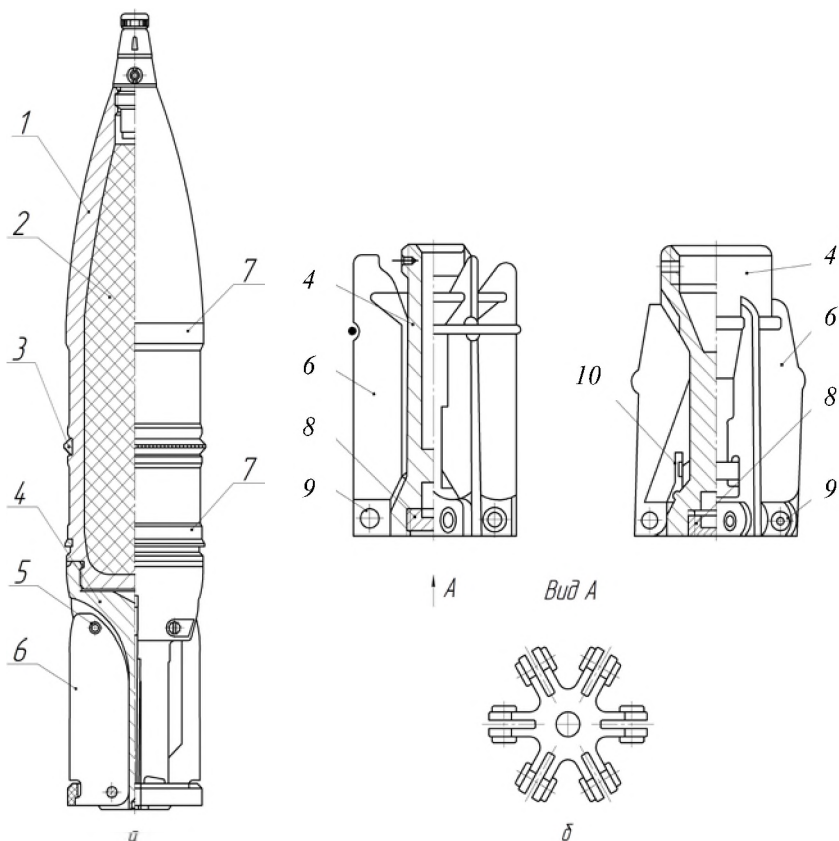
Оперенный снаряд с раскрывающимся стабилизатором второго типа (а) и разновидности раскрывающихся стабилизаторов первого типа (б); 1 – корпус снаряда; 2 – разрывной заряд; 3 – обтюрирующий пояс; 4 – корпус стабилизатора; 5 – стопорный винт; 6 – лопасть стабилизатора; 7 – центрующие утолщения; 8 – трассерная гайка; 9 – ось вращения лопасти стабилизатора; 10 – стопорное кольцо
